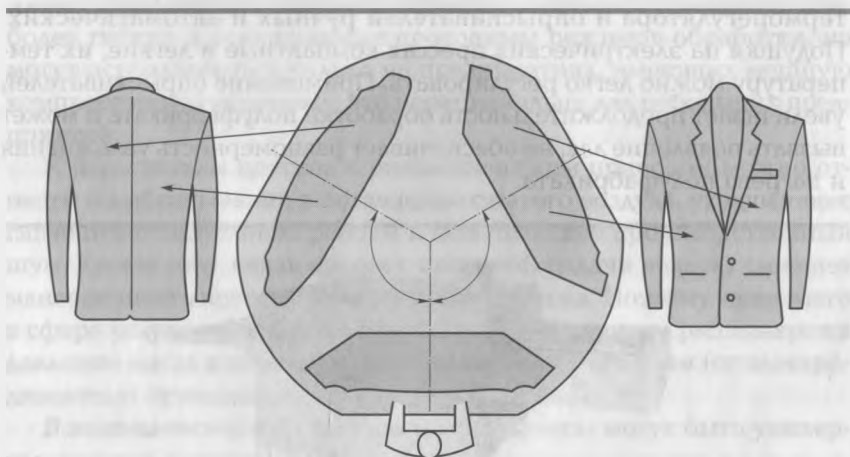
Схема действия карусельного прессы для приутюживания деталей переда и спинки
